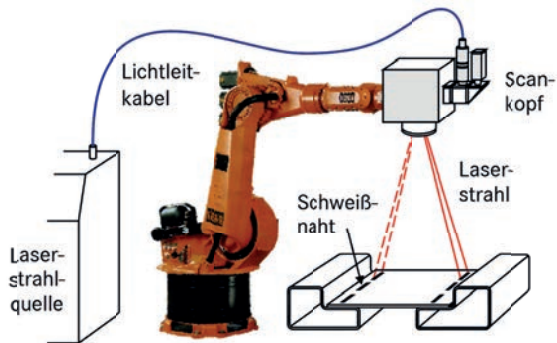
Robotergeführtes Remote-Schweißen mit modernen Festkörperlaser (Faser- oder Scheibenlaser): Funktionsbeschreibung und Komponenten [Quelle: Daimler].
